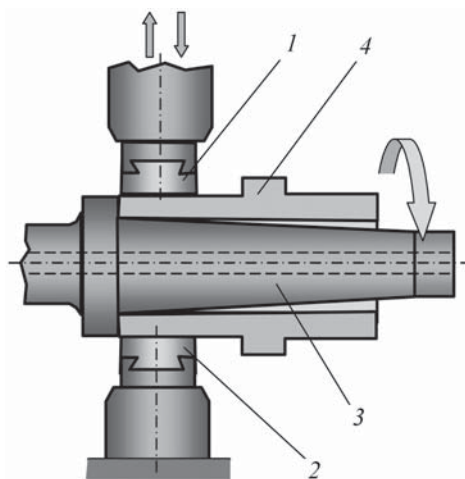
Схема протяжки пустотелой заготовки на конической оправке:
